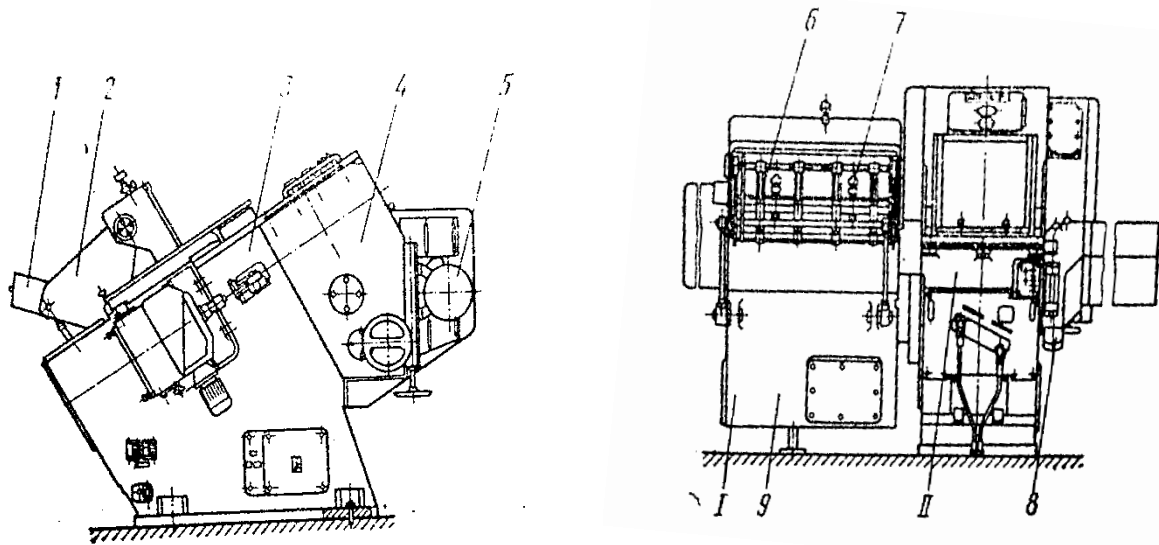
Кривошипний прес для виготовлення жерстяних банок РКХД 63.2
